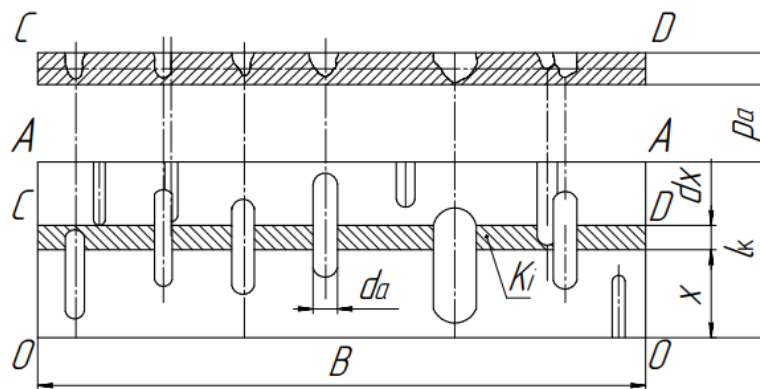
Схема для ймовірнісного розрахунку опорної довжини профілю поверхні різання в зоні контакту круг-заготовка
